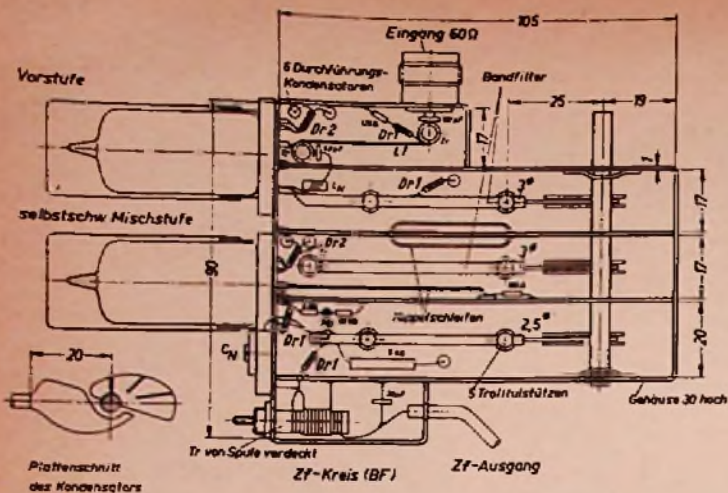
Konstruktionszeichnung des Dezi-Tuners nach Bild 7
